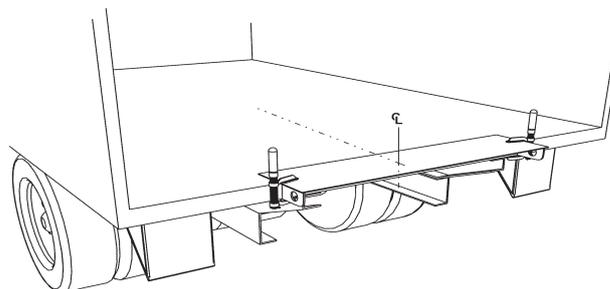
Atornillar o soldar por puntos el accesorio de montaje en la barra trasera, N° de ref. 74632TL para Z3N 75
